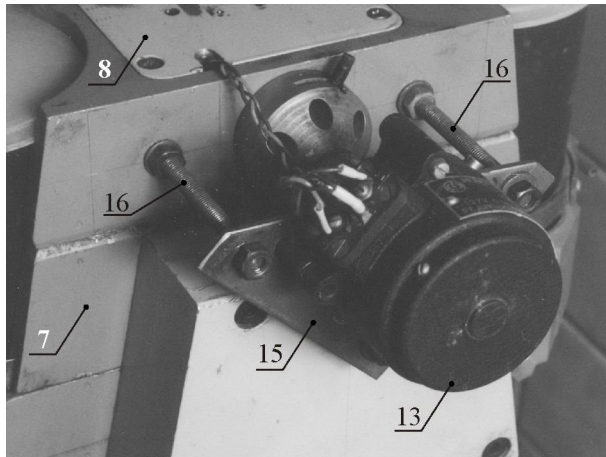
Фото елементів системи автоматичного керування рухомими дебалансами віброверстату ВІО-8
